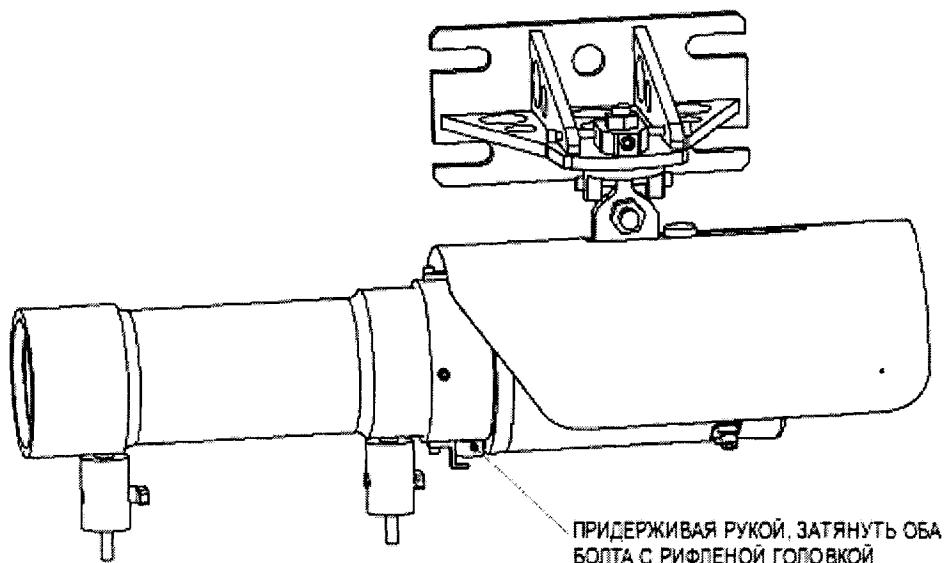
Схема установки кюветы газовой на передней фланец излучателя или приемника
